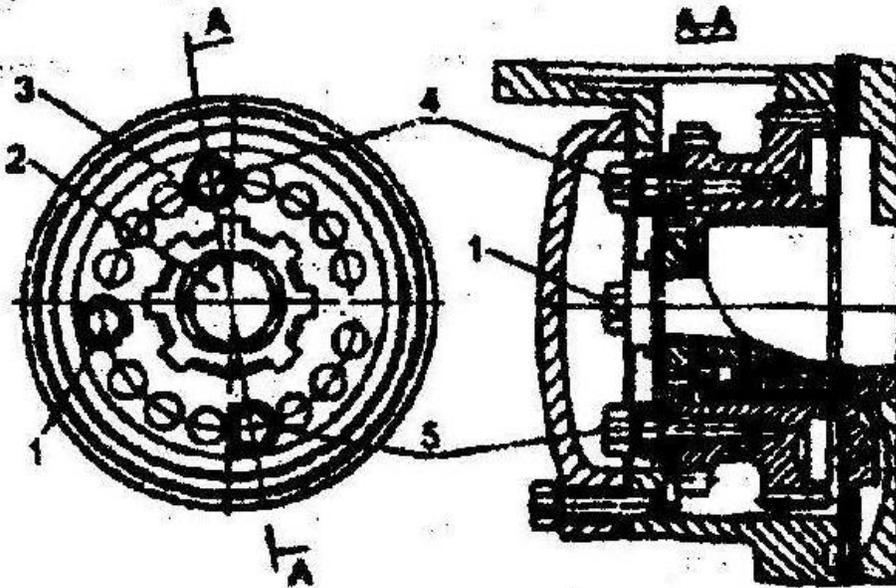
Регулировка угла начала подачи топлива на двигателе Д-245
